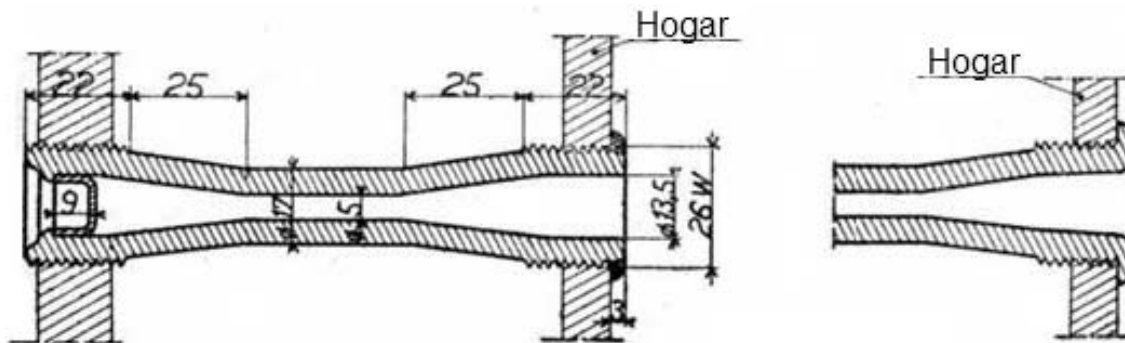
Virotillo alemán modelo Henschel, mandrilada con ayuda de un aparato especial y remachado o soldado con autógena de la parte del hogar
